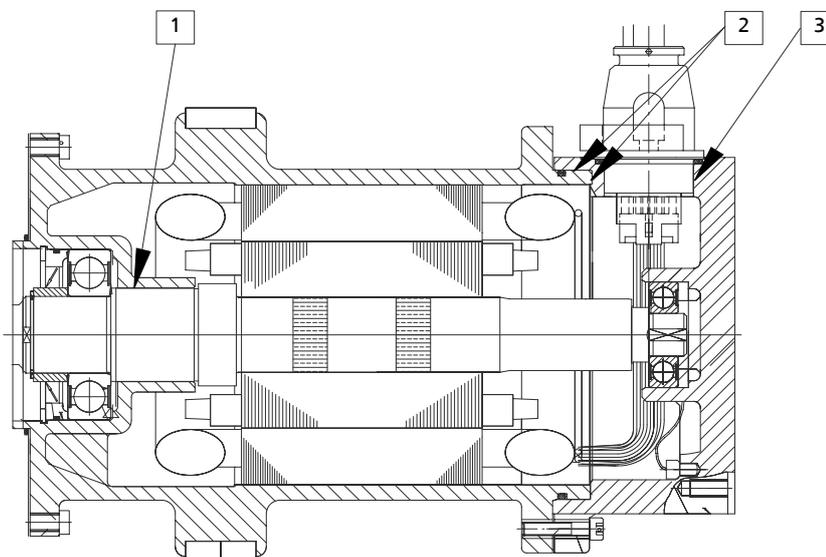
Ex-Spaltflächen bei explosionsgeschützten Motoren - Motortyp DKM90 / 112 und MA09 / 11
